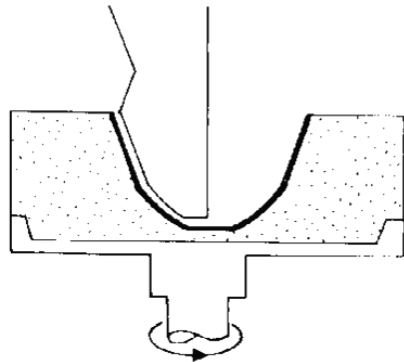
Visão esquemática de um processo de torneamento (*Jolleying*).
